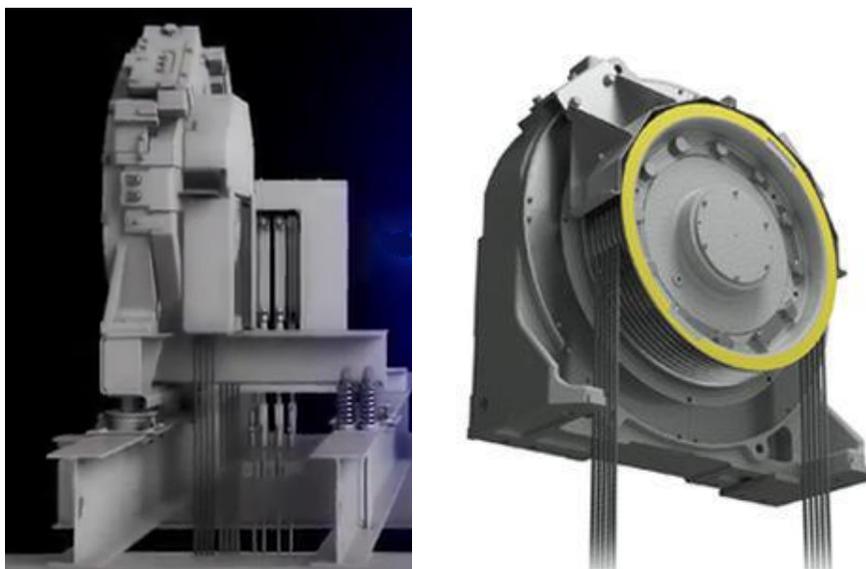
Conjunto Tractor para equipo con sala de máquinas y sin sala de máquinas
